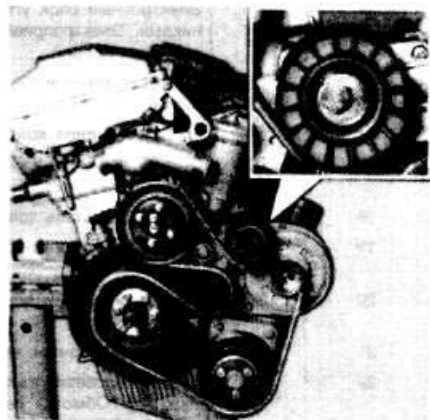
Расположение регулировочного болта натяжителя ремня привода генератора автомобилей с 6-цилиндровым бензиновым двигателем
